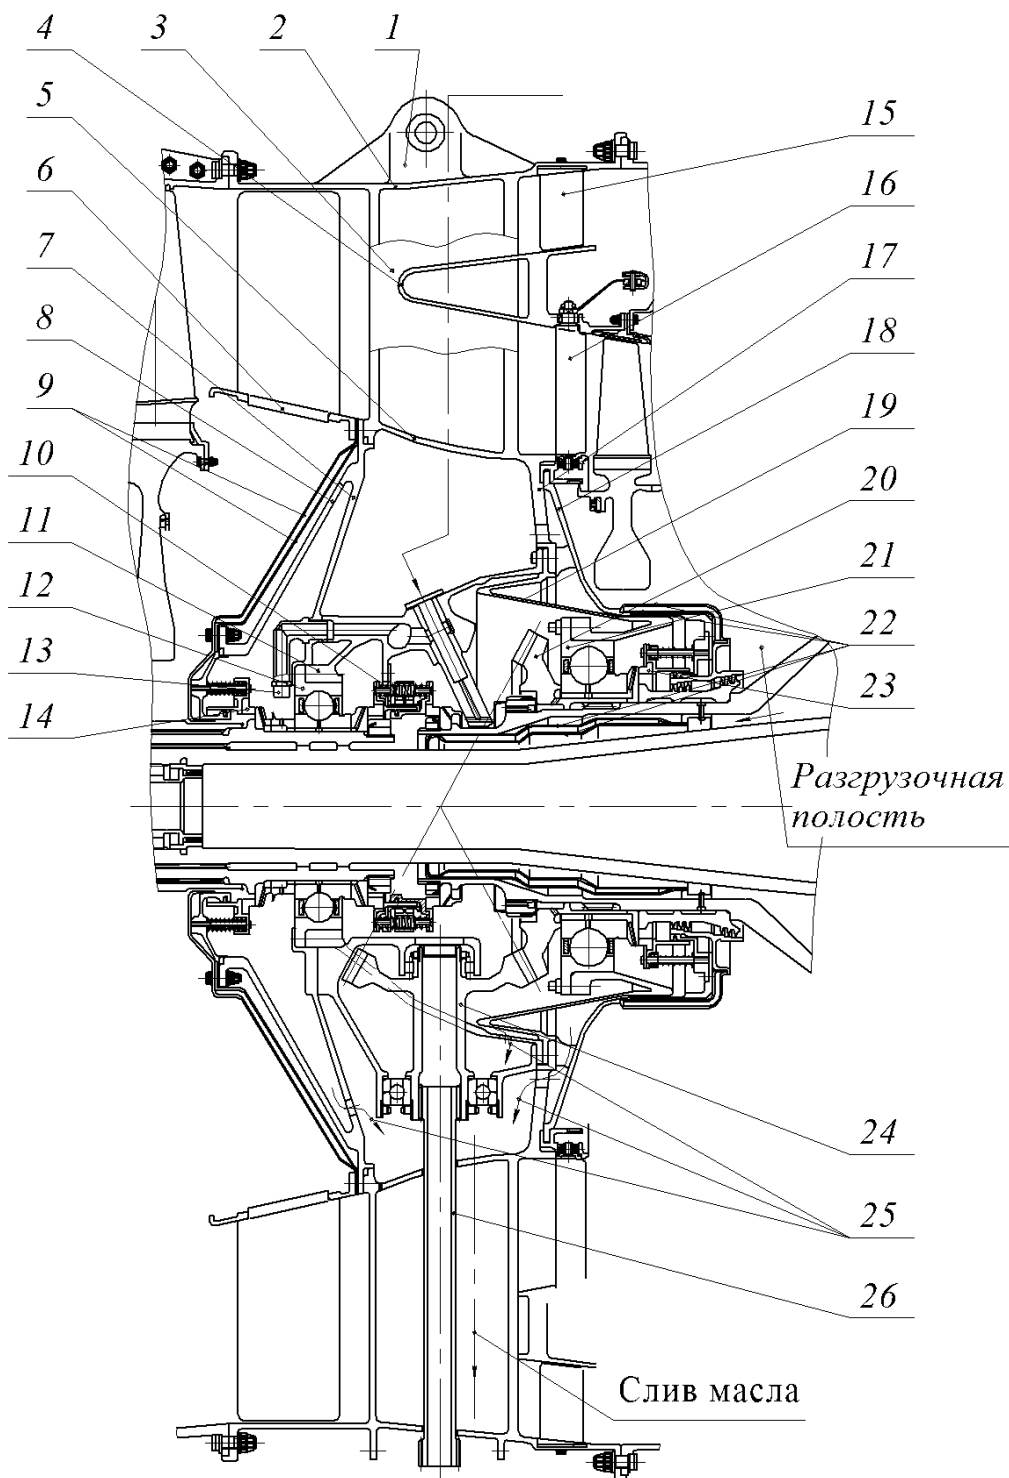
Средняя опора ТРДДФ F100-PW-229, конструкция и конструктивная схема:
